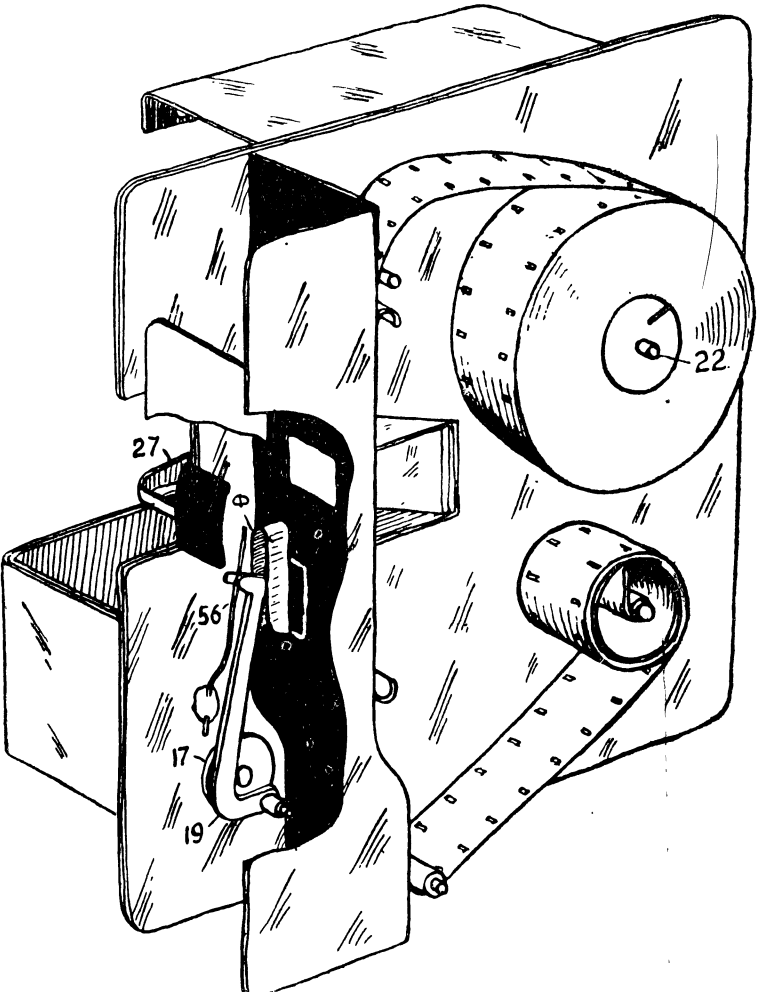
Механизм со стороны съёмной крышки. Направляющая скобочка Ф припаивается к фильмовому каналу, пружина 56 — к панели
